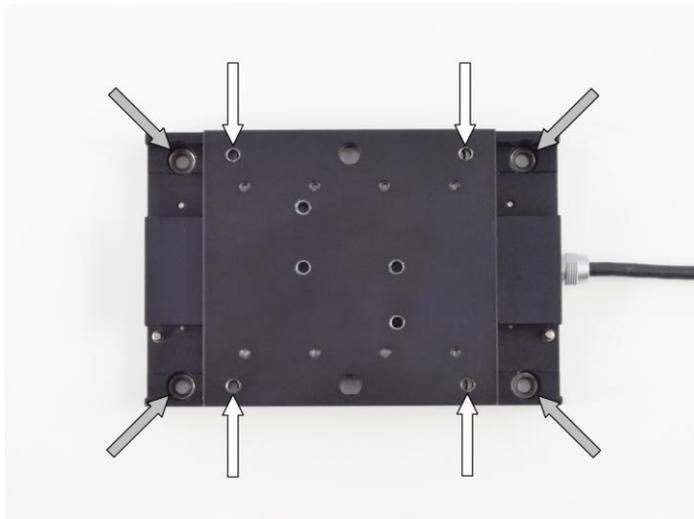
Gewindebohrungen für die Adapterplatte (weiße Pfeile) und Senkbohrungen im Grundkörper (graue Pfeile)
